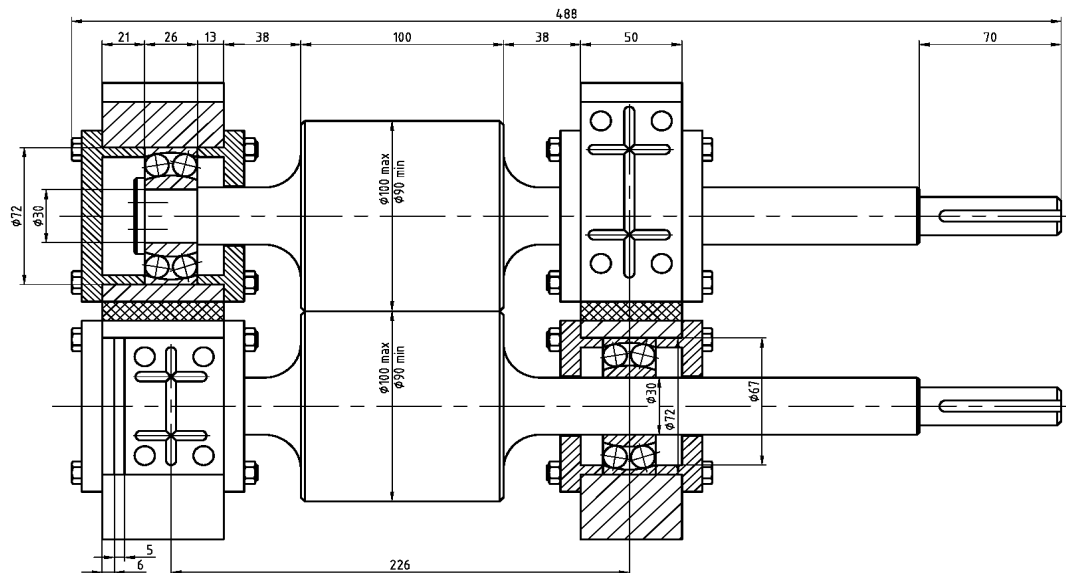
Конструкція вузла робочих валків лабораторного прокатного міні-стану 260x260 .
